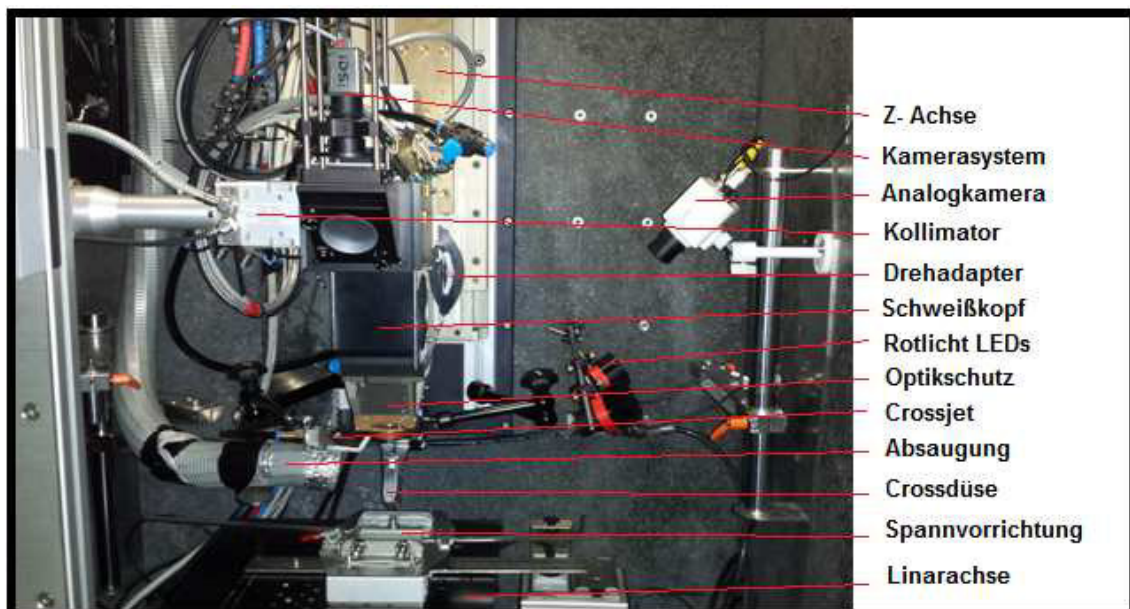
Anordnung des experimentellen Versuchsaufbaus für Schweißversuche
